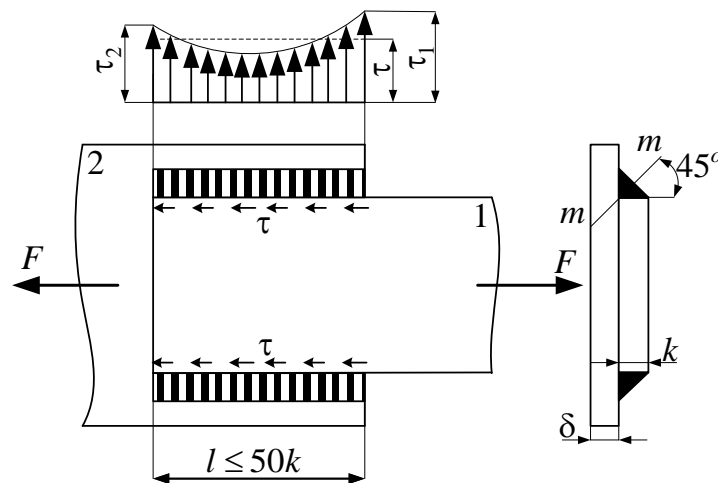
Схема сварного соединения с фланговыми швами
